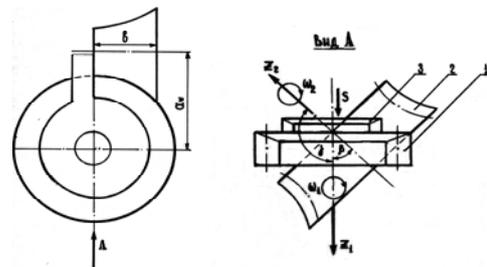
Изготовление и отделка квазигиперболического колеса и обкаточного инструмента
